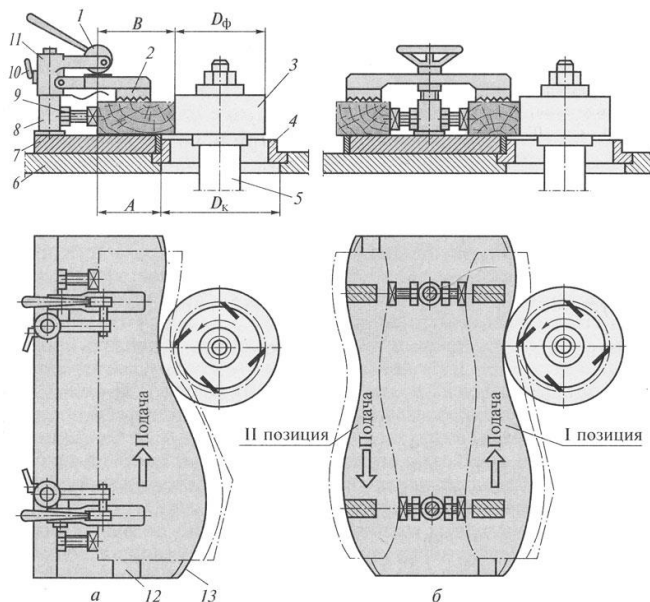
Схема криволинейной обработки на фрезерном станке с помощью шаблона: а – одноместного; б – двухместного; 1 – эксцентриковый прижим; 2- прижимная колодка; 3- фреза; 4- копирное кольцо; 5- шпиндель; 6 – стол станка; 7- корпус шаблона; 8- стойка; 9- базирующий упор; 10- фиксатор прижима; 11- кронштейн; 12- торцовый упор; 13- стальная лента
